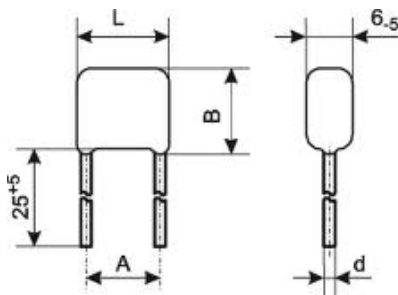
Габаритні розміри резистора типу СПЗ-38А
